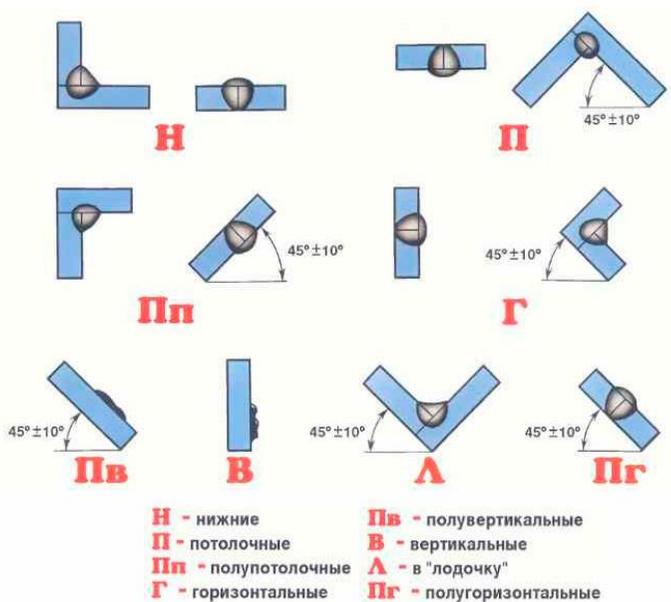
Виды сварки по расположению в пространстве и протяженности
